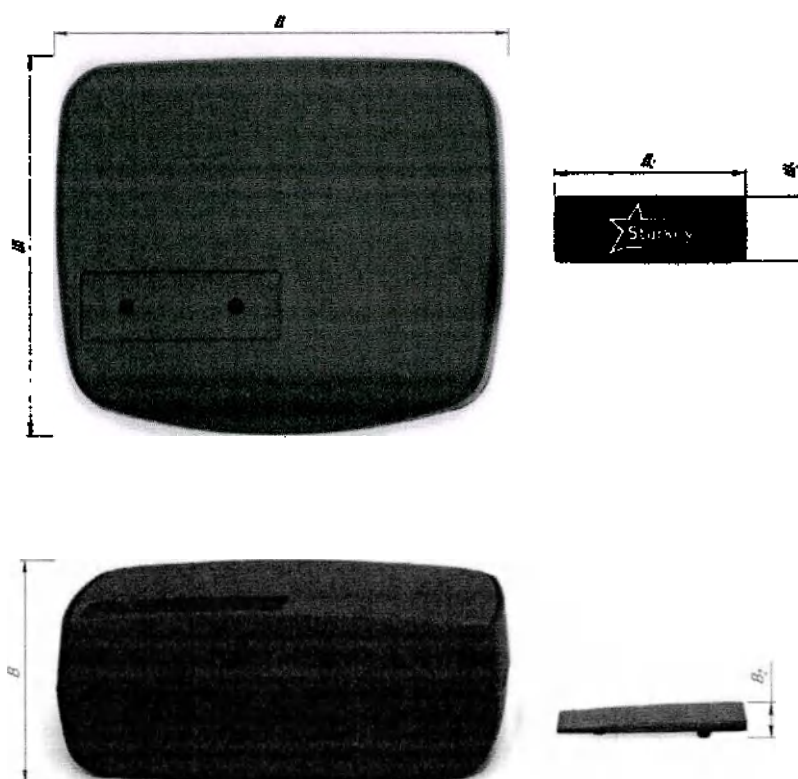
Внешний вид и размеры футляра пластикового с биркой STARKEY
